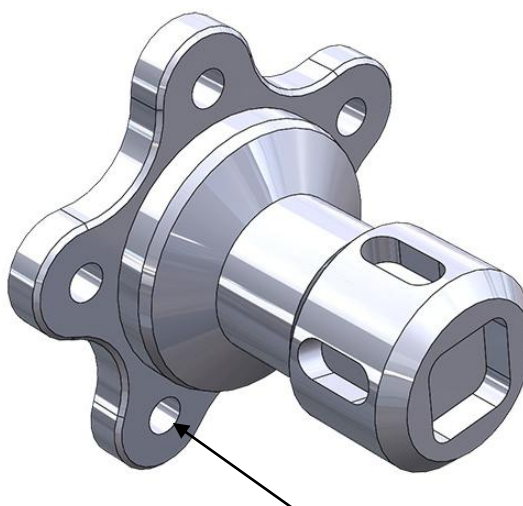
Praktická ukázka výrobku s axiálním frézováním [20]
